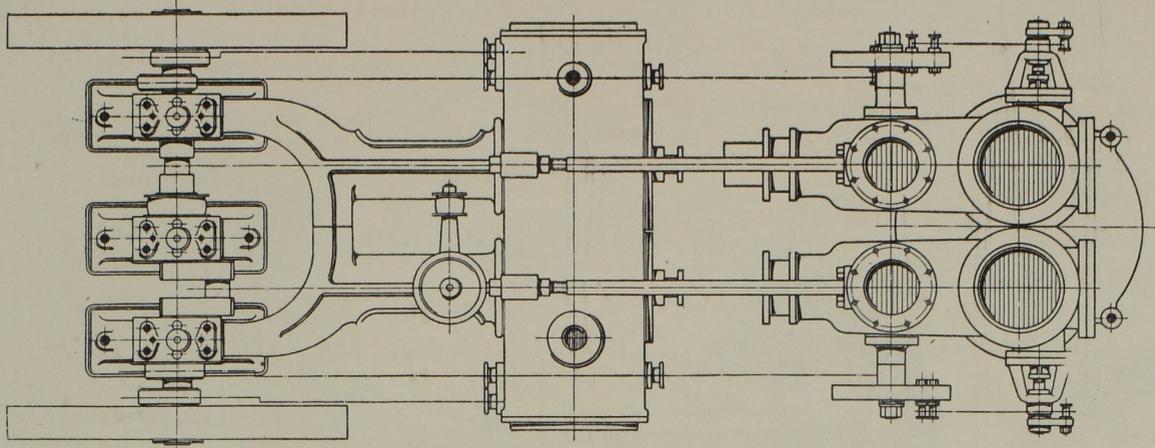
Grundriss der Pumpmaschine. Massst. 1 : 32.
